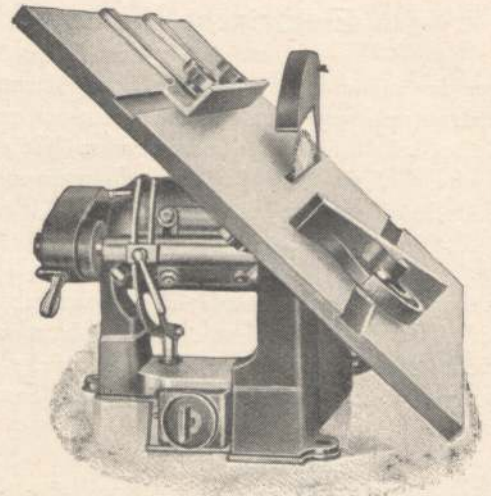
Dieselbe Maschine mit schräggestelltem Tisch. Das Gewicht obenstehender Maschine beträgt 90 kg.
